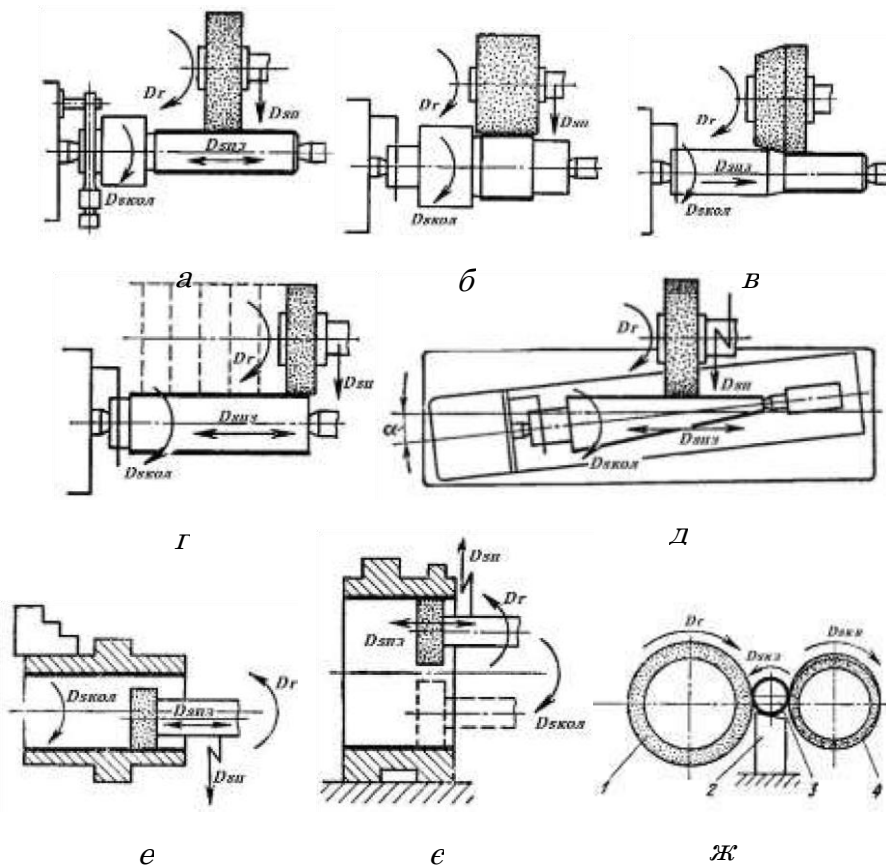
Схеми оброблення заготовок на круглошліфувальних верстатах
